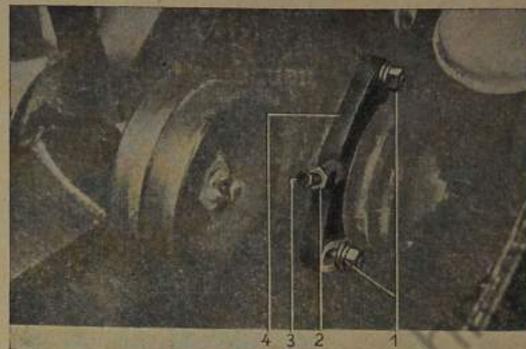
Hinteren Lagerbock für Gelenkwelle abschrauben
